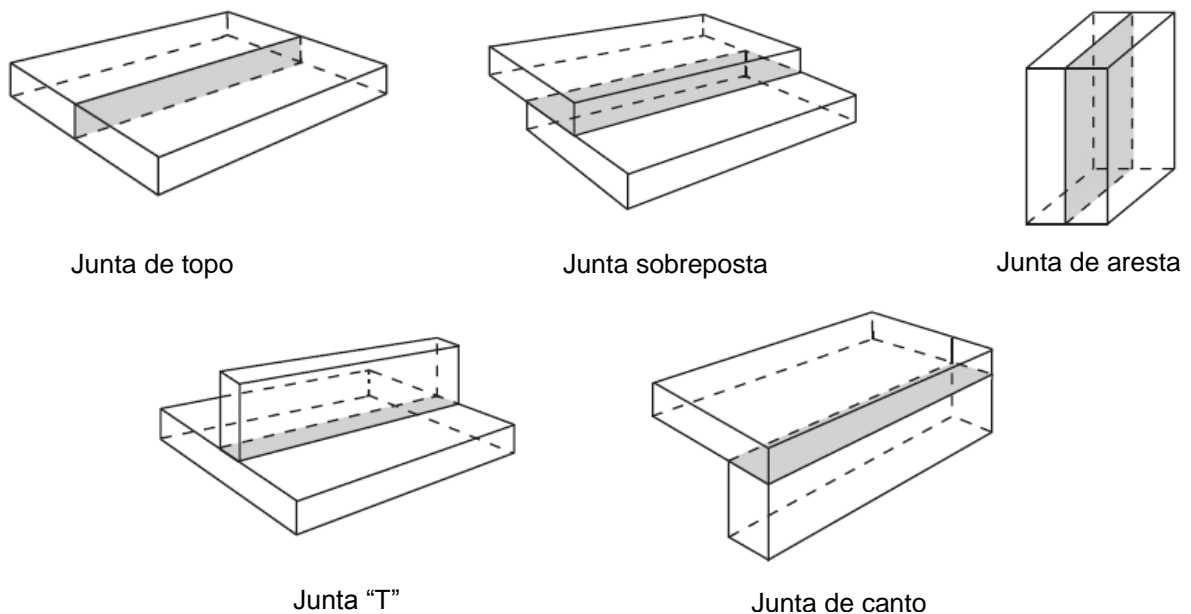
Principais tipos de juntas utilizadas em soldagem.
